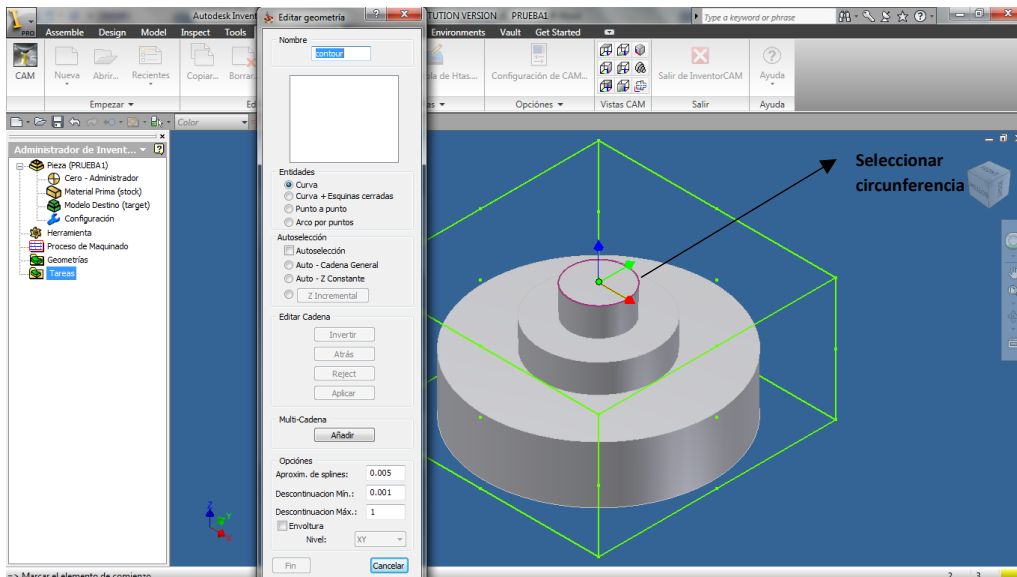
Maquinado Fresadora CNC – Selección de circunferencia para perfil
